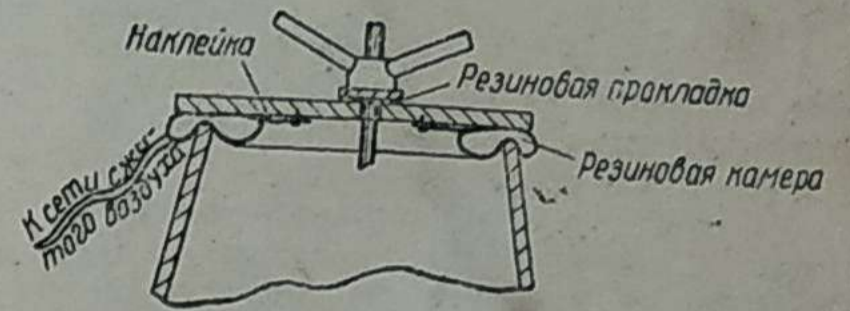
Приспособление для проверки герметичности швов бункера сжатым воздухом.
